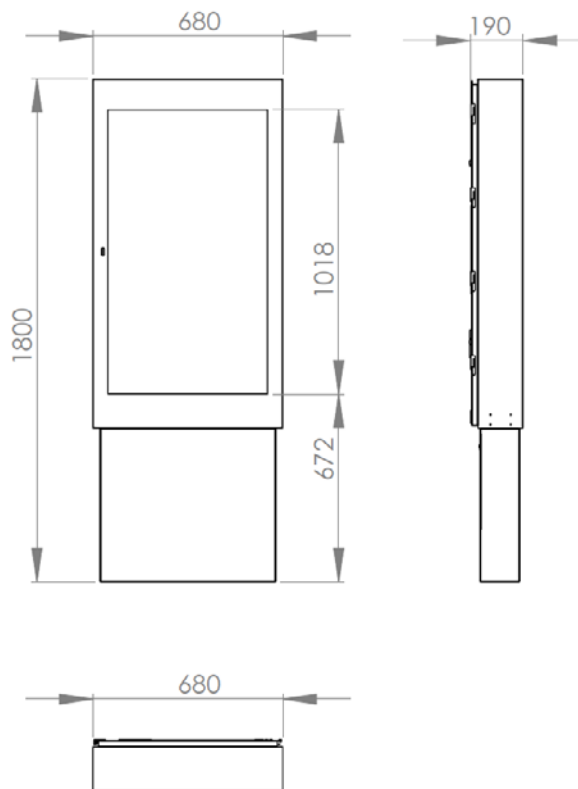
DIB 600 PREMIUM, Dimensioni in mm
